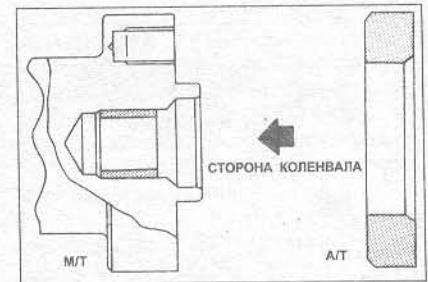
Детали установки втулки направляющего подшипника коленвала (Глава 18)
